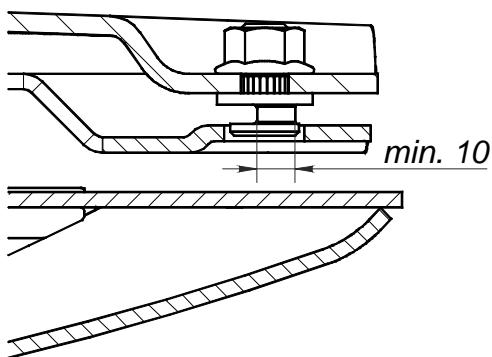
Допускаемое изношение стержня держателя ножей в диске
